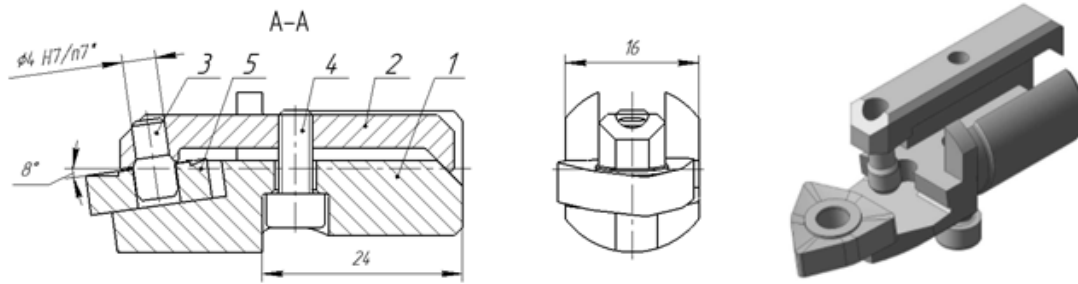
Блок резцовый: 1 – державка; 2 – прихват; 3 – штифт; 4 – винт; 5 – пластина режущая
